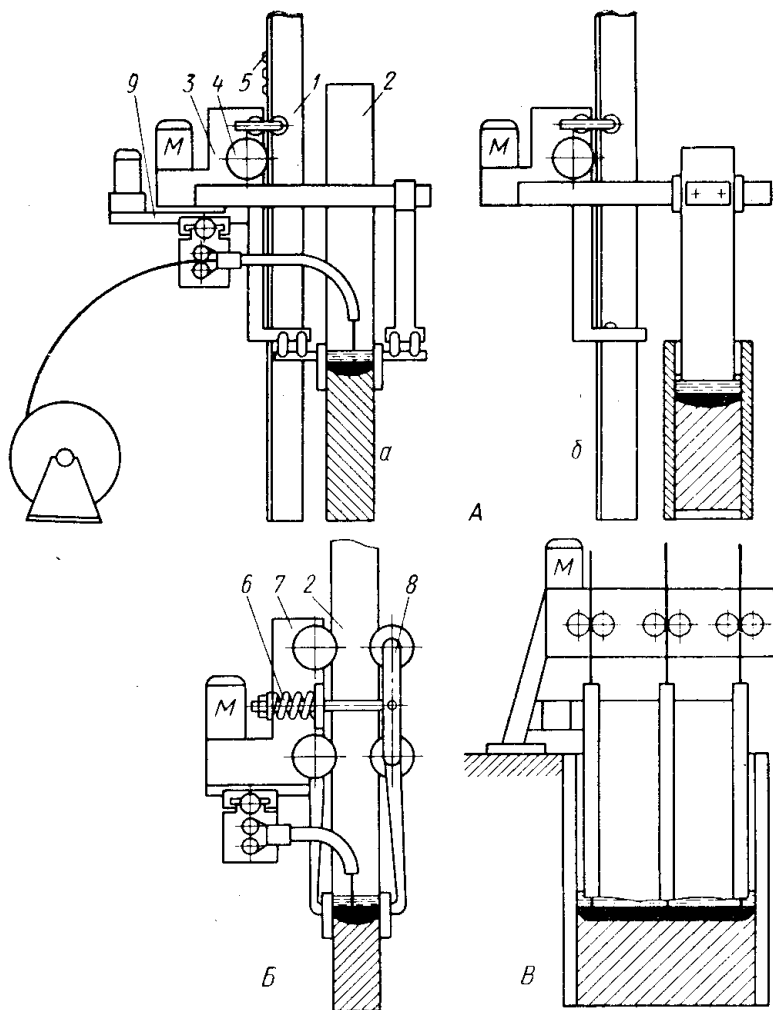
Аппараты для электрошлаковой сварки:
